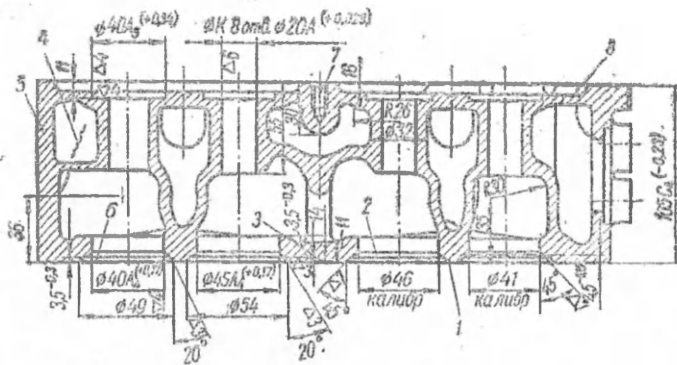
Головка блока цилиндров двигателя СМД-7 (разрез по клапанным гнездам).
